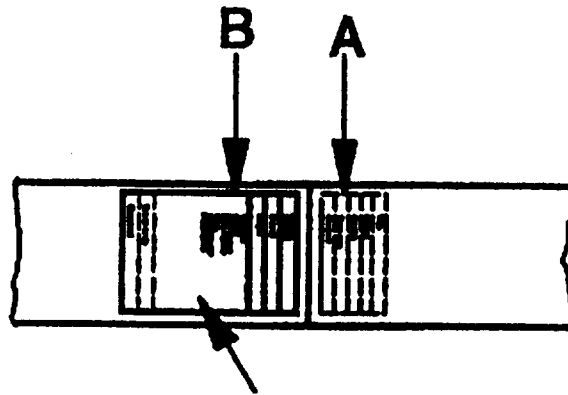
Typische Befestigung des Etiketts an einem Endloshebeband
